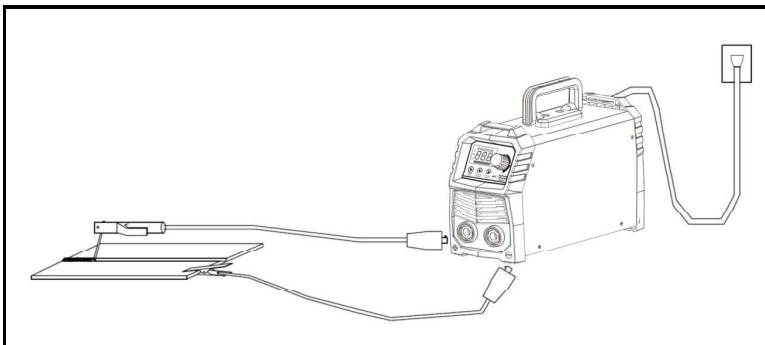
Schéma de la soudure MMA – Electrode enrobée
